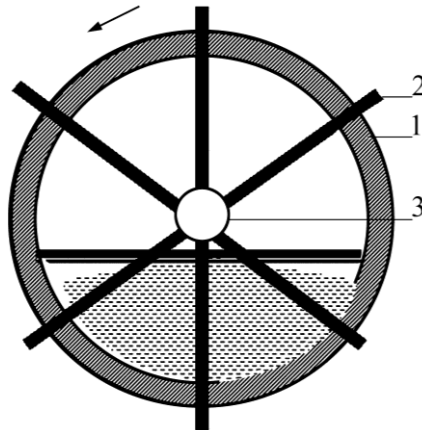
Установка для ПЭХТО во вращающейся ванне: 1 – барабан; 2 – обрабатываемая деталь; 3 – контактная втулка [129].
